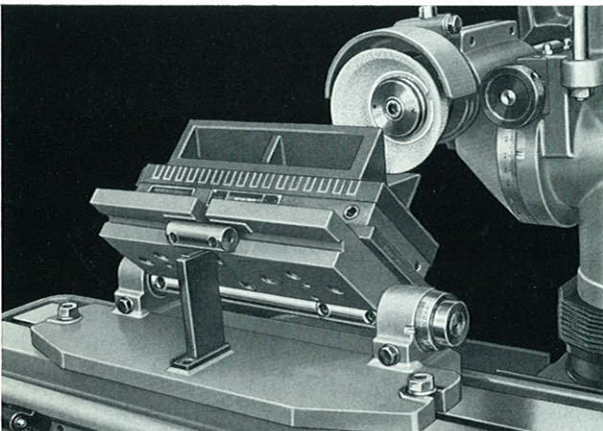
Schleifen einer schrägen Fläche an Werkstück, aufgespannt auf Magnetplatte mit schwenkbarem Plattenträger
